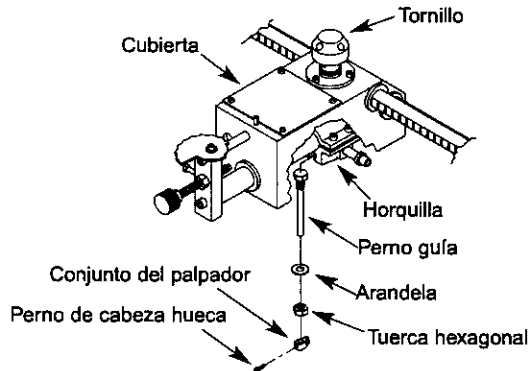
Instale el Perno Guía y el Conjunto del Palpador
